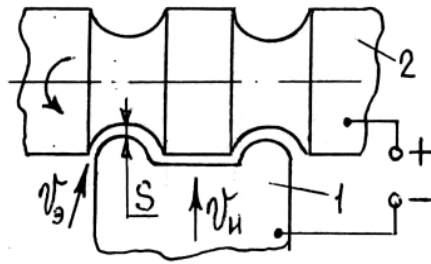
Схема точіння зовнішніх поверхнь: 1 – електрод-інструмент; 2 – заготовка
